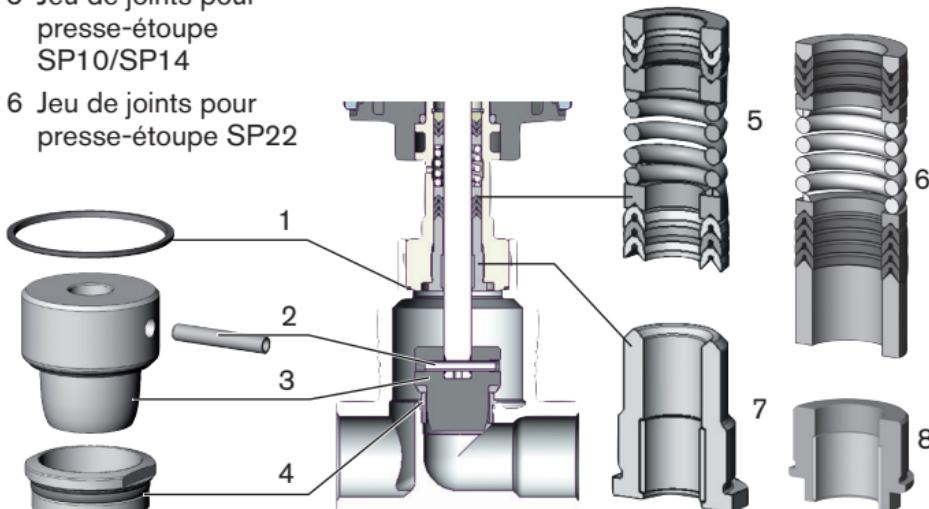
Pièces de rechange pour vanne de réglage à siège droit
